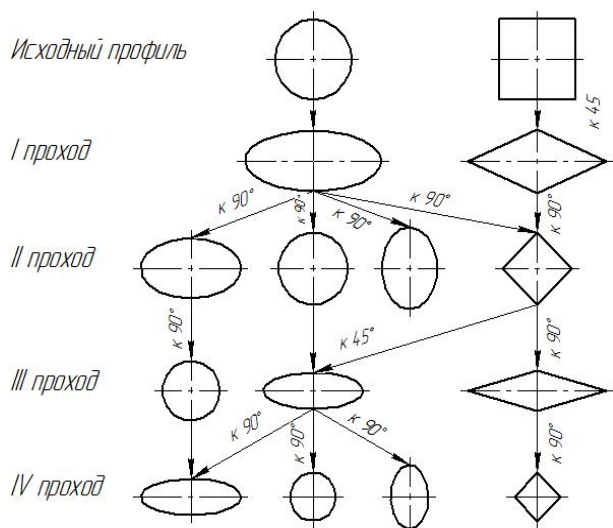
Схема вальцовки из круглой и квадратной заготовки [1]
